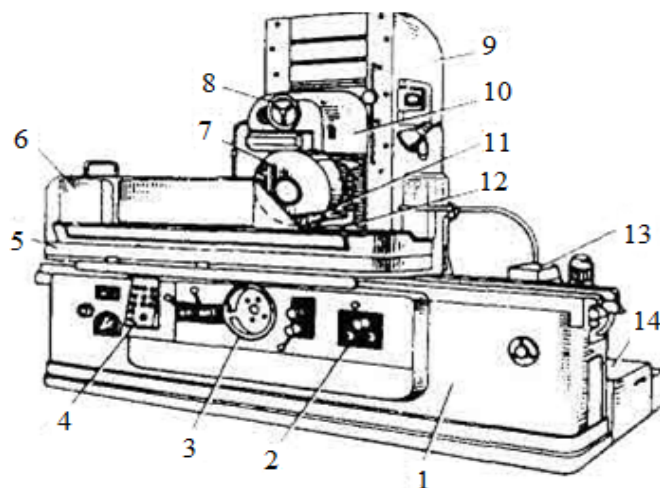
Загальний вигляд плоскошліфувального верстата:
